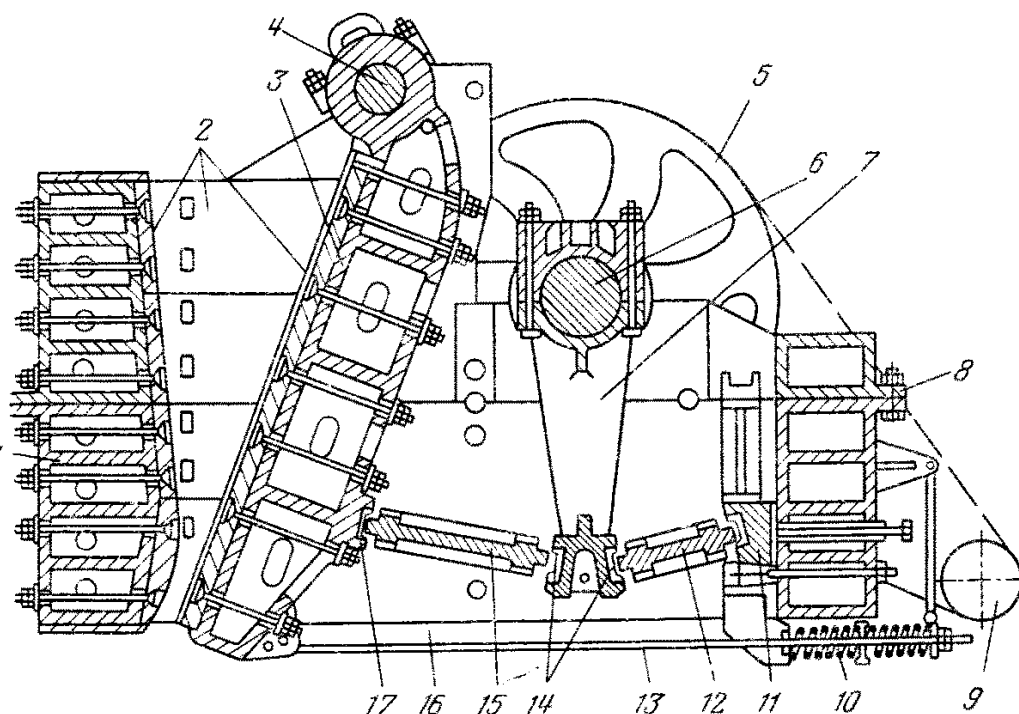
Принципова схема щоківі дробарки з простим рухом щоки:
